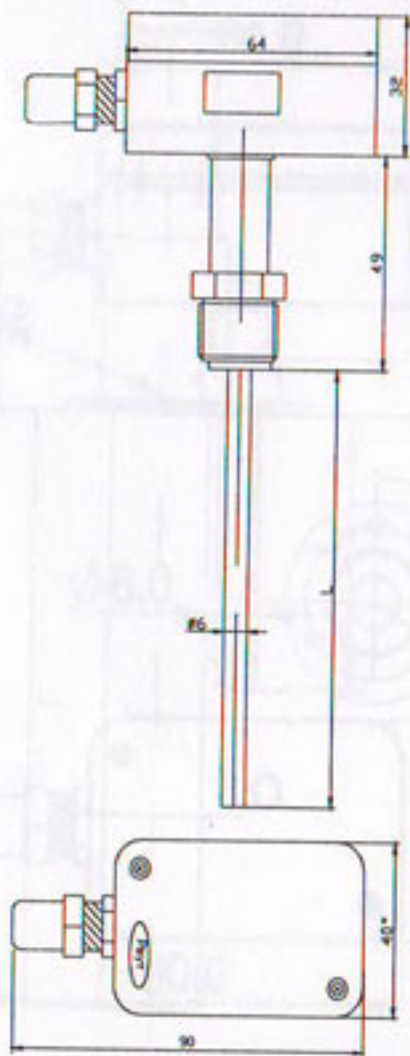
Конструктивные особенности и габаритно-присоединительные размеры датчика СТв-01
